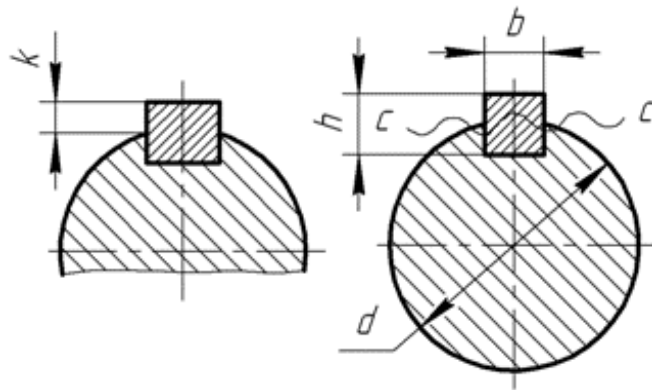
Розрахункова схема шпоночного з'єднання
